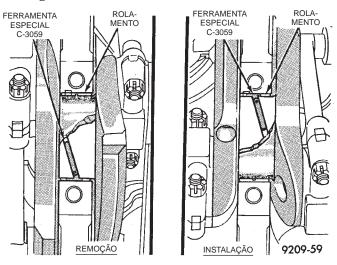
Remoção e Instalação do Rolamento Principal Superior com a Ferramenta C-3059
